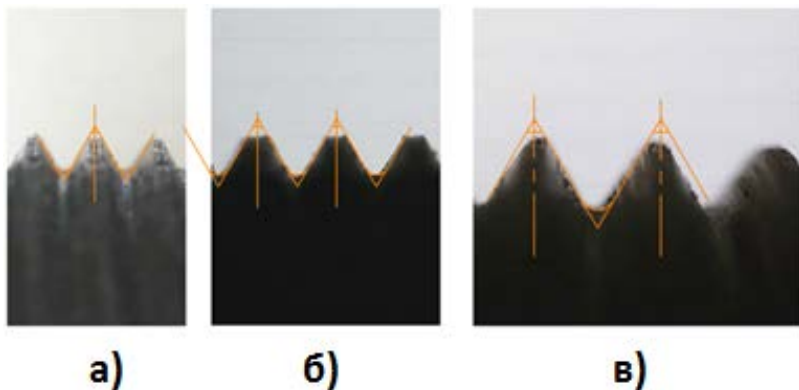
Теоретический и нарезанный профили резьбы:
